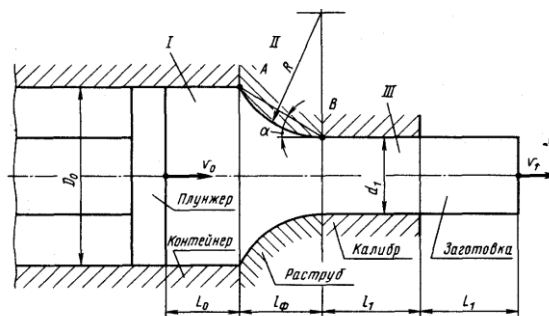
Схема пресового інструменту для екструзії електродних заготовок
